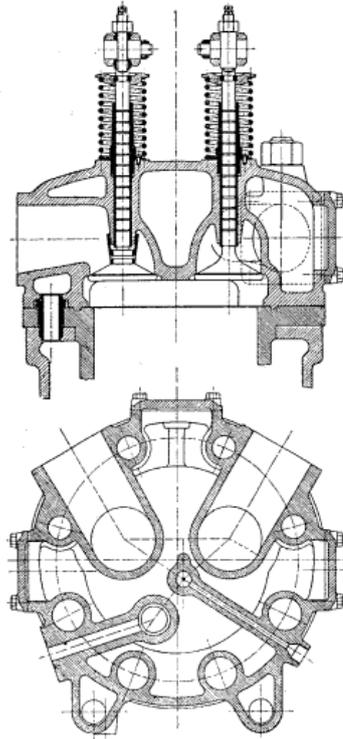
Couvercle des cylindres du moteur du *Frerichs*.
